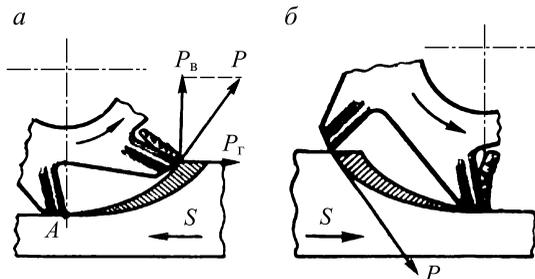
Встречное (а) и попутное (б) фрезерование цилиндрической фрезой
